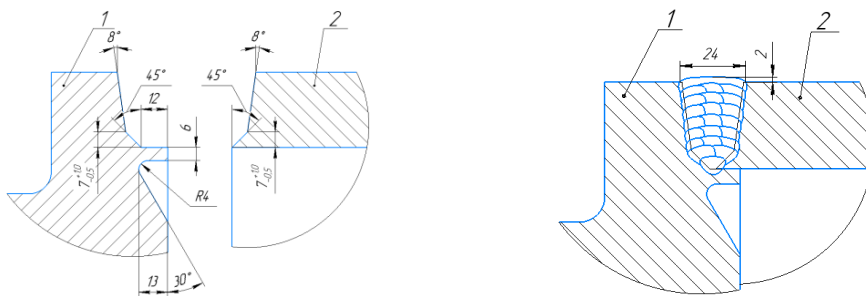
Форма разделки кромок и сварного шва
